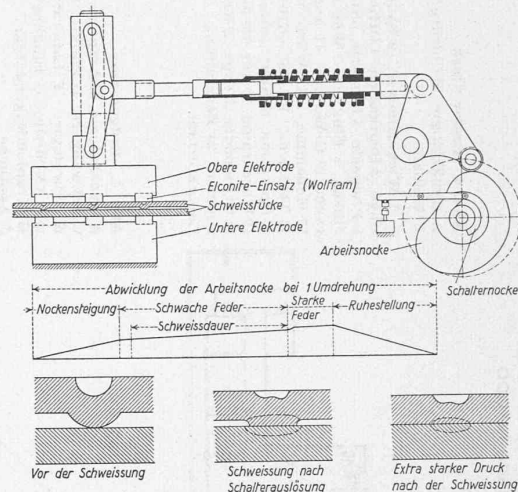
Schema der Arbeitsweise einer Buckel-Schweissmaschine
